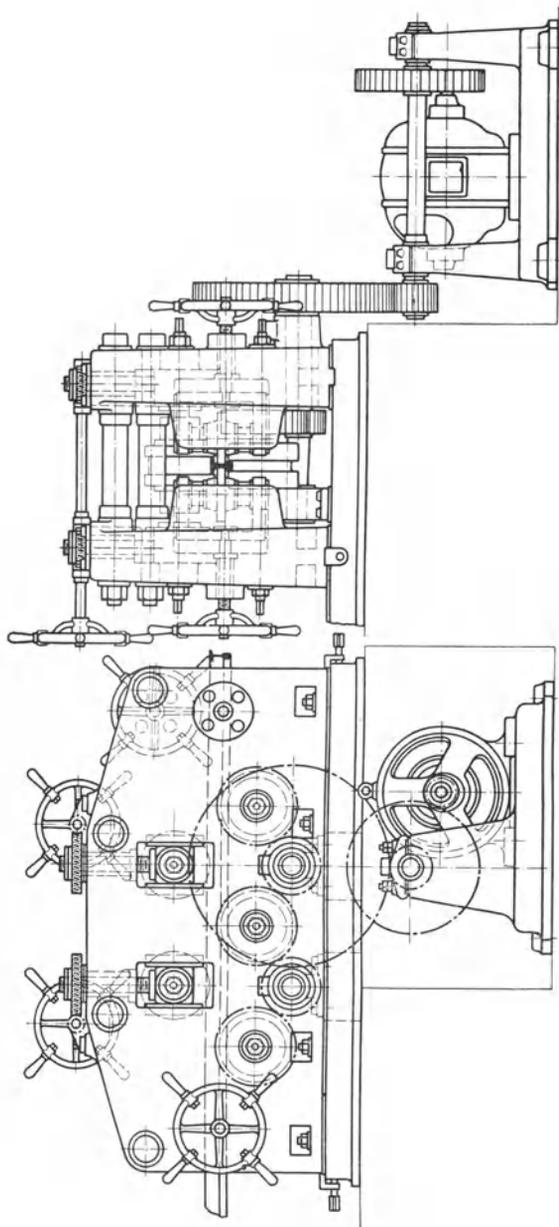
Mitteleisenrollenrichtmaschine mit schwer auswechselbaren Richtrollen.
